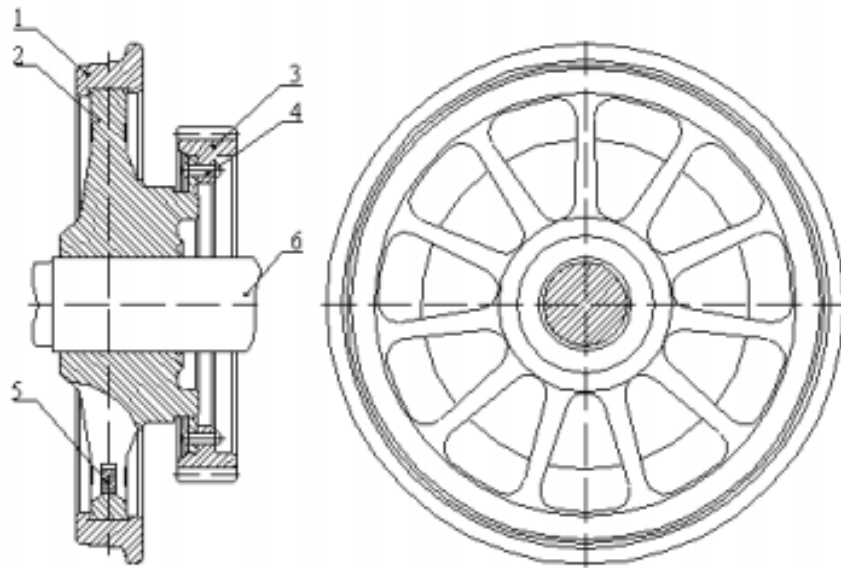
Колесо електровагону з зубчастим вінцем, сполученим заклепками з фланцем маточини: 1 - бандаж; 2 - центр; 3 - вінець зубчастий; 4 - заклепка; 5 –пластина зміцнююча; 6 – вісь [11].
